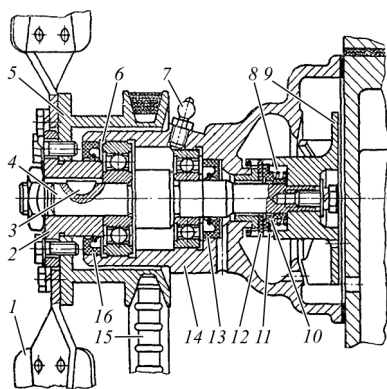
Центробежный жидкостный насос: 1 – вентилятор; 2 – ступица; 3 – сегментная шпонка; 4 – вал насоса; 5 – шкив; 6 – стопорное кольцо; 7 – масленка; 8 – упорная пружина сальника; 9 – крыльчатка насоса; 10, 13, 16 – сальники; 11 – обойма; 12 – уплотнительная шайба; 14 – корпус насоса; 15 – клиновидный ремень
